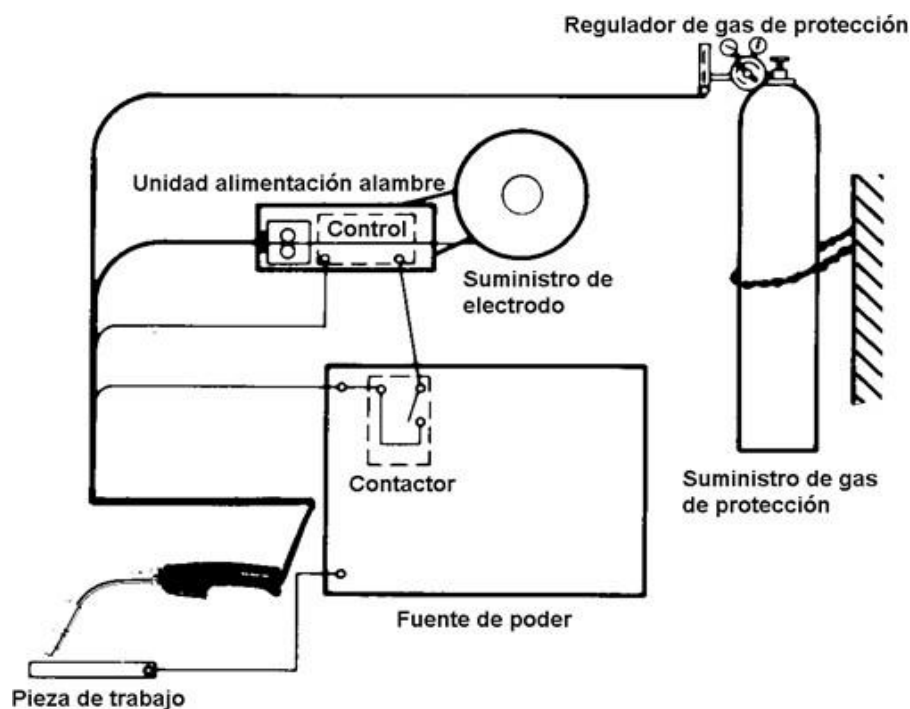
Equipo de Soldadura GMAW [13]
